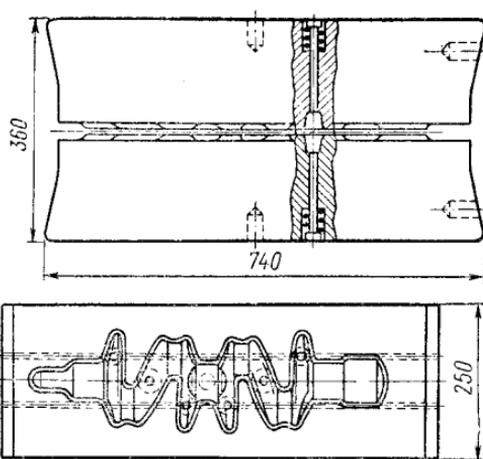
Окончательная вставка для штамповки поковки коленчатого вала с противовесом
